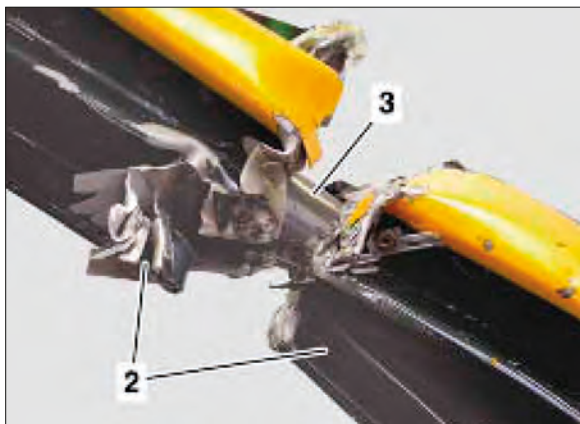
Montante A (2) y tubo de refuerzo (3)
